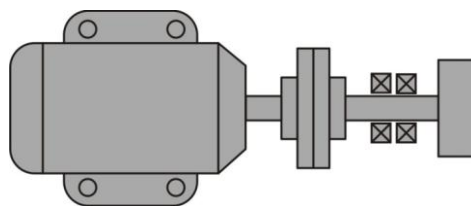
Схема для определения потерь на трение в подшипниках быстроходного вала шестерни
